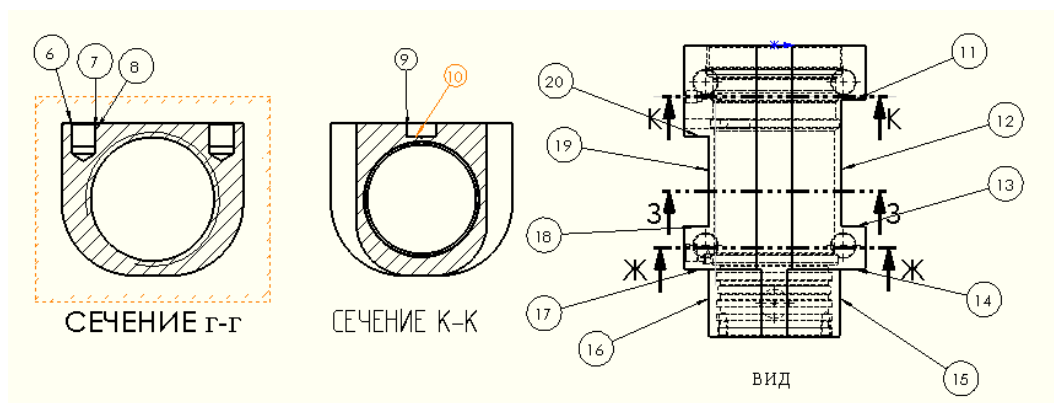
(Б) – Ескіз корпусу з нумерацією поверхонь
